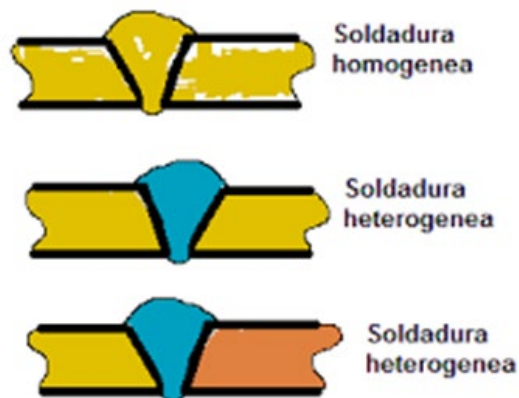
Soldaduras homogénea y heterogénea con diferentes materiales de aporte
